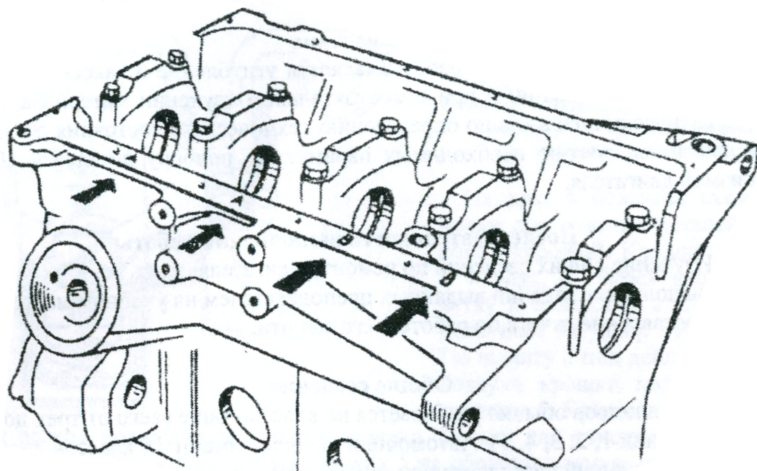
Буквенная маркировка размерного класса цилиндров на блоке двигателя
